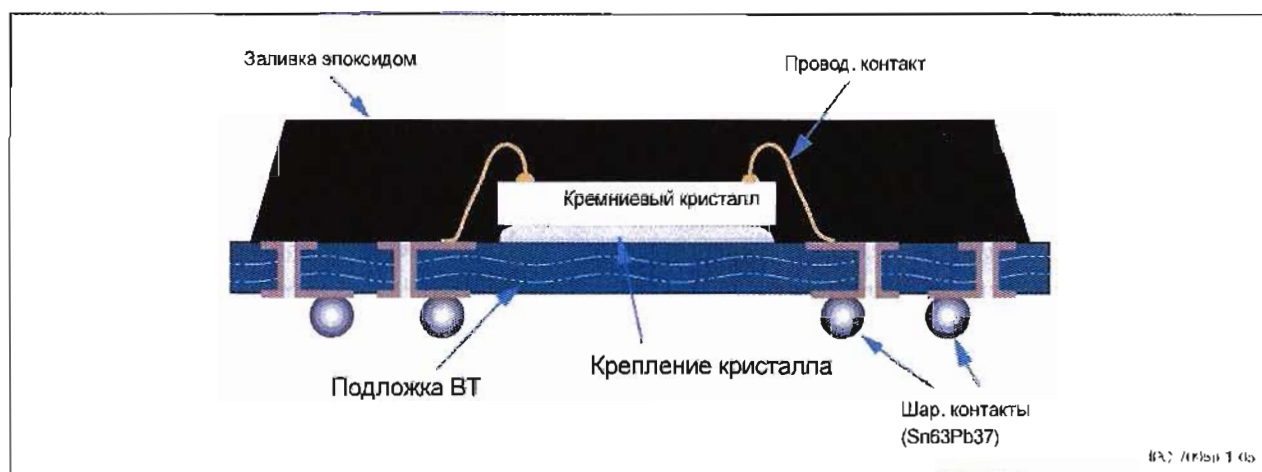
Пластиковый корпус BGA, кристалл с рываркой проволоочных соединений
